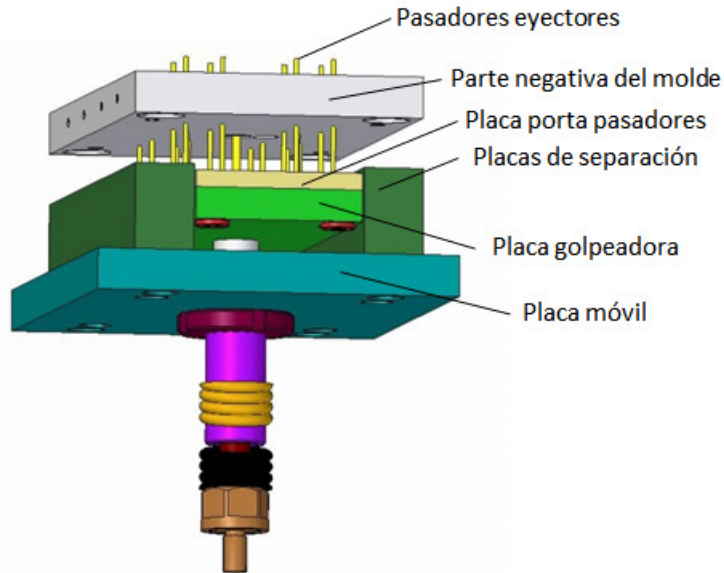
Sistema de eyección para molde de inyección (Modificada de [33]).
